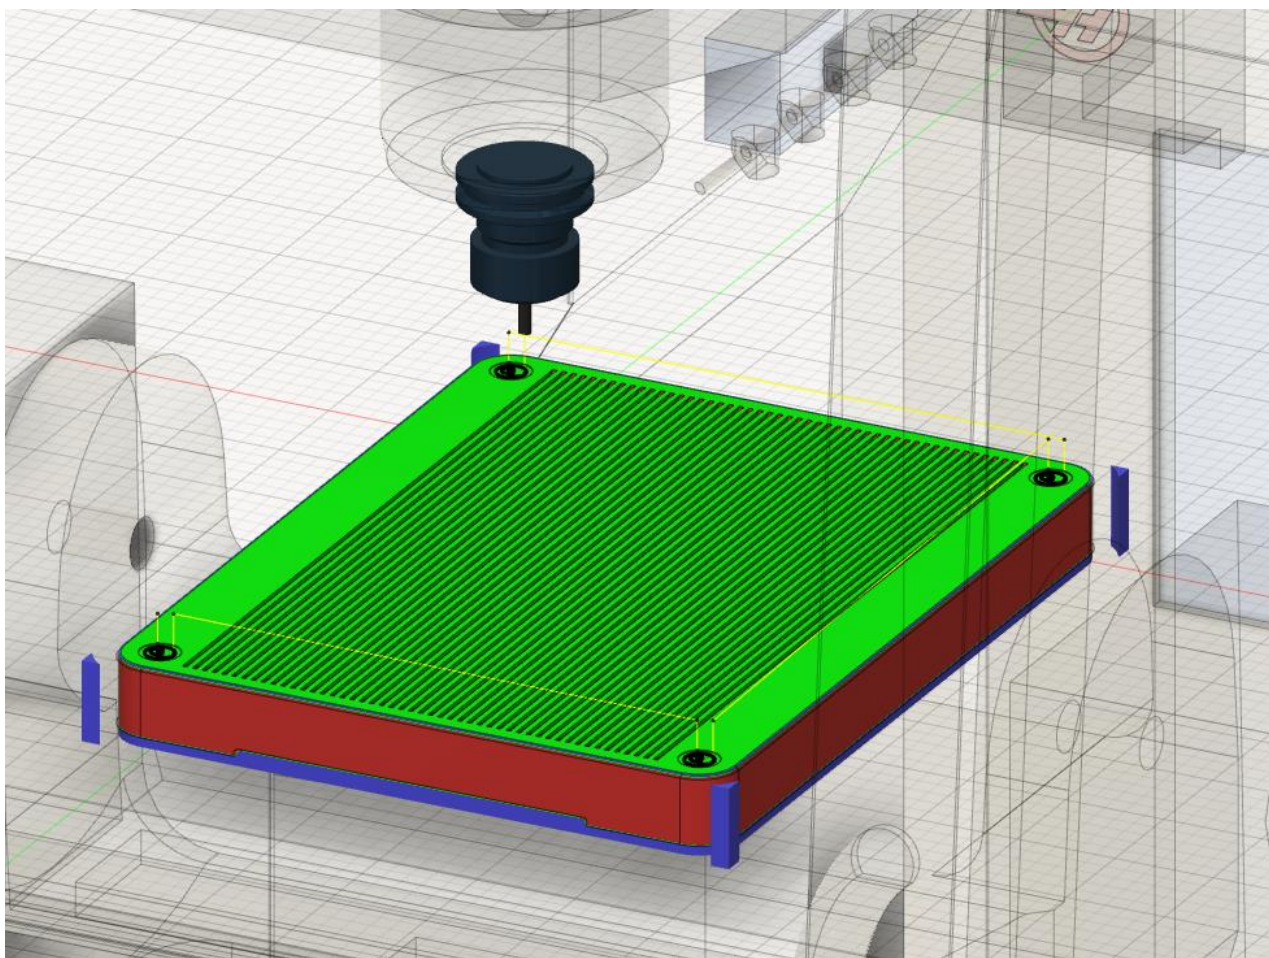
Операція 010 - Обробка заглиблень ніжок
